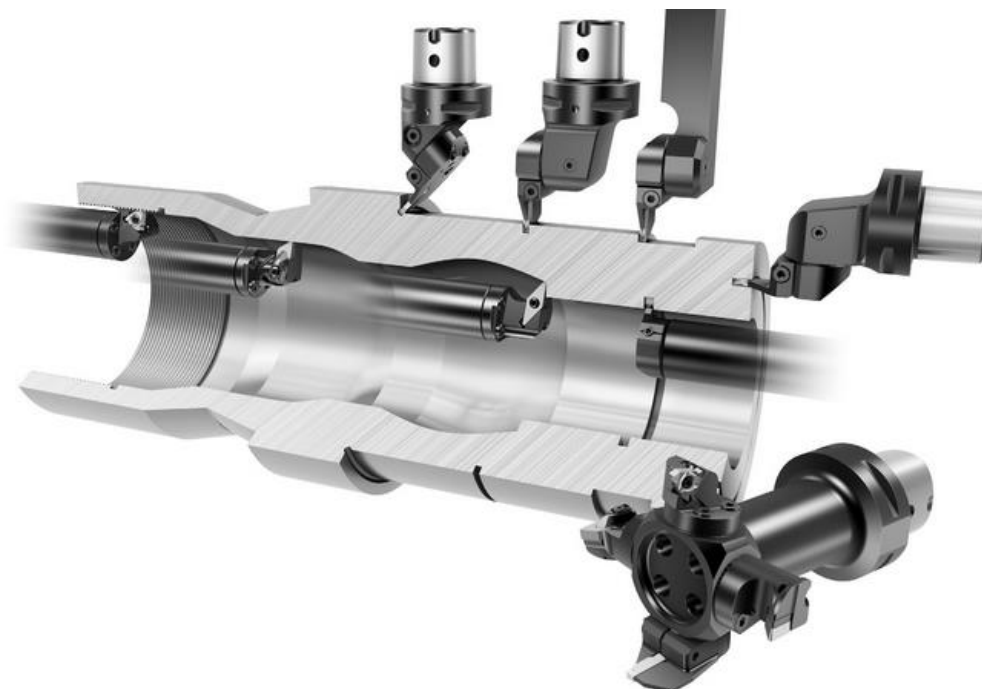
Способи обробки канавок деталі типу «пустотілий вал»
